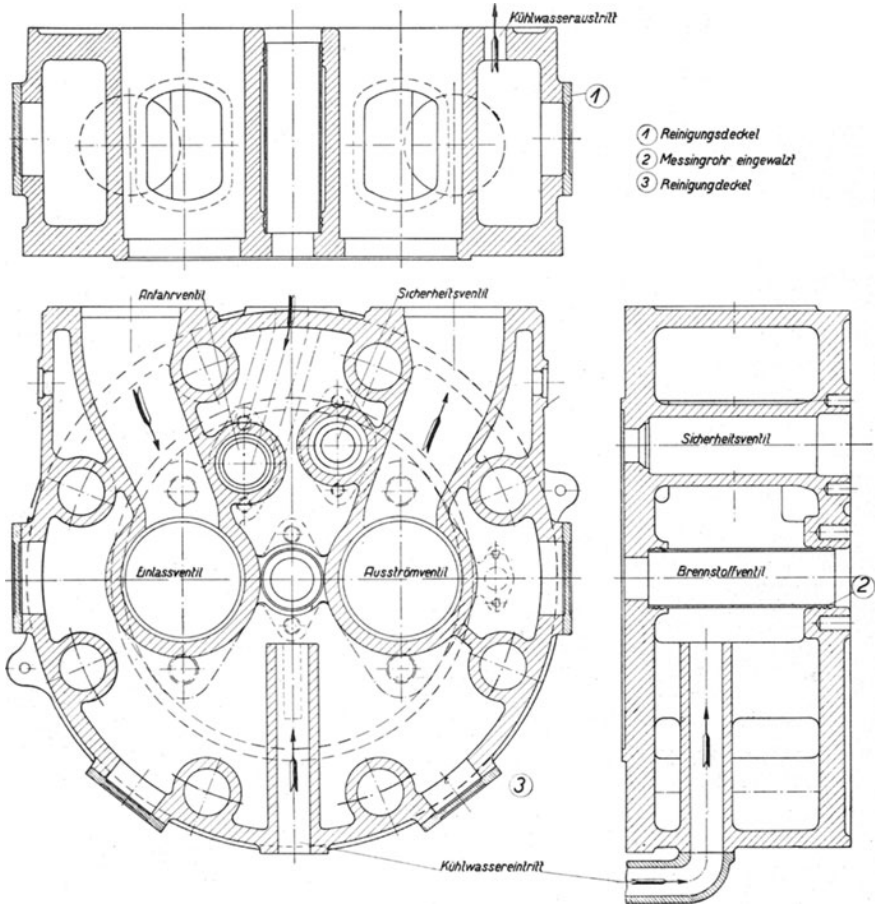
25. Zylinderdeckel einer Viertakt-Ölmaschine.
